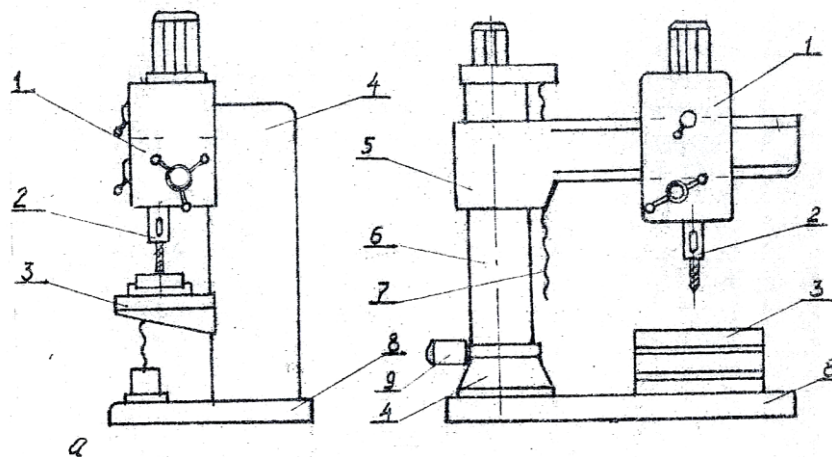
Вертикально-свердлувальний (а) та радіально-свердлувальний верстати (б).
